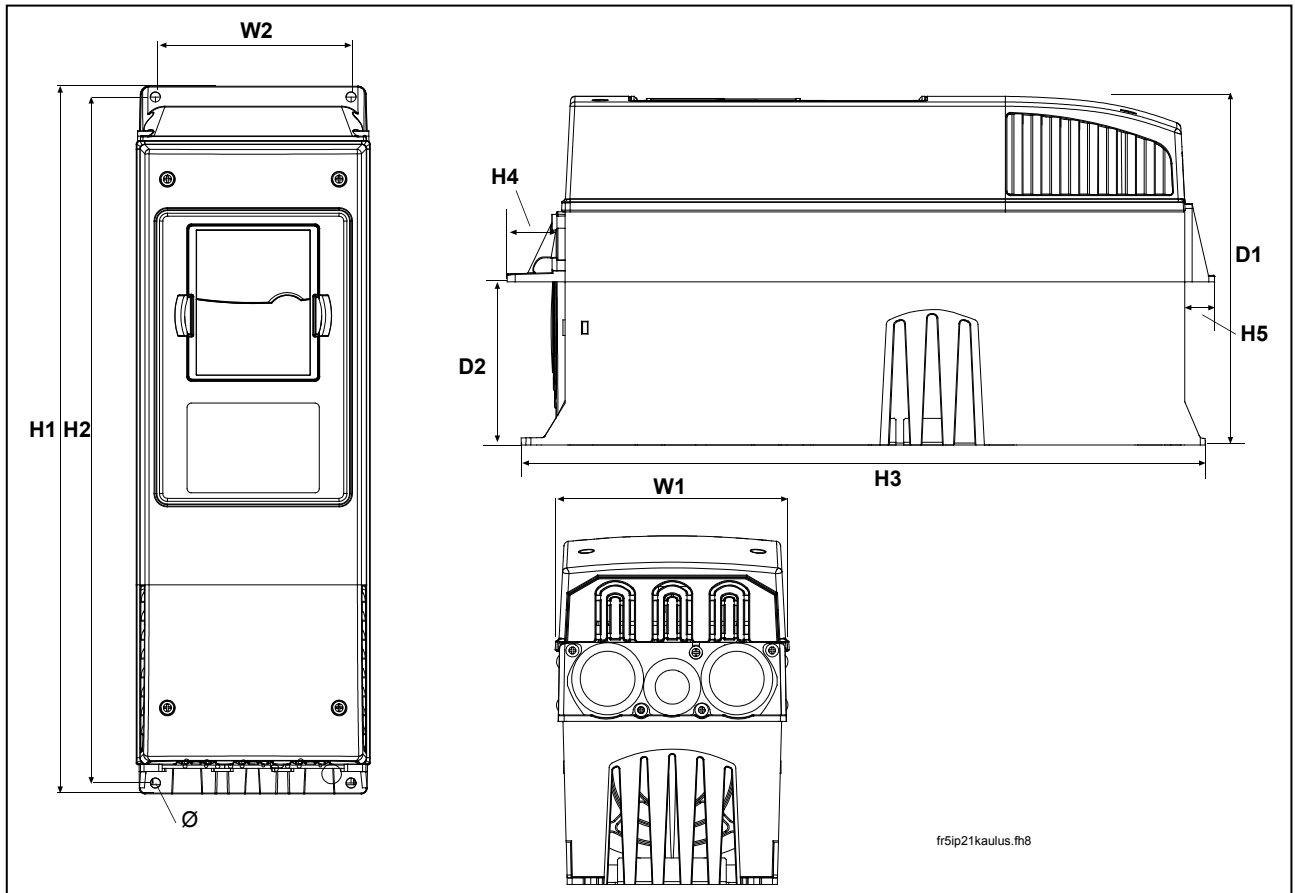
Габариты инвертора Vacon NX, IP21, с фланцем, FR4 и FR6
